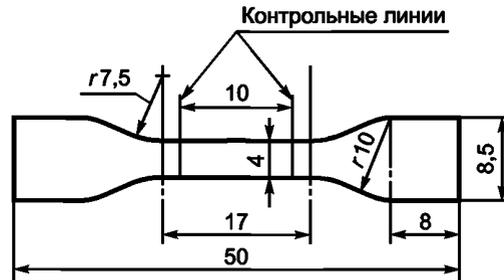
Образец в виде двусторонней лопатки уменьшенного размера
